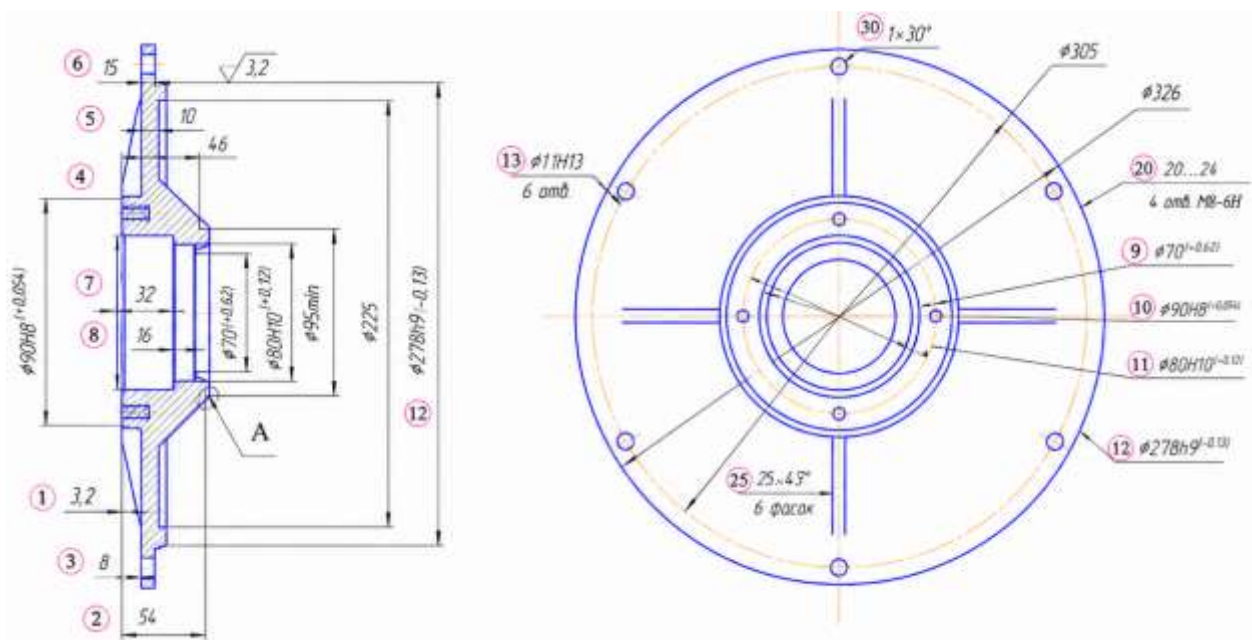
Основні поверхні деталі «Кришка редуктора КС6Б-0.01»
